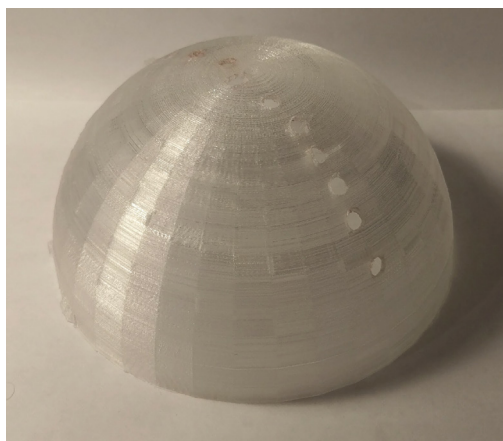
Корпус прототипа трекера, изготовленный из PLA-пластика с помощью трёхмерной печати
